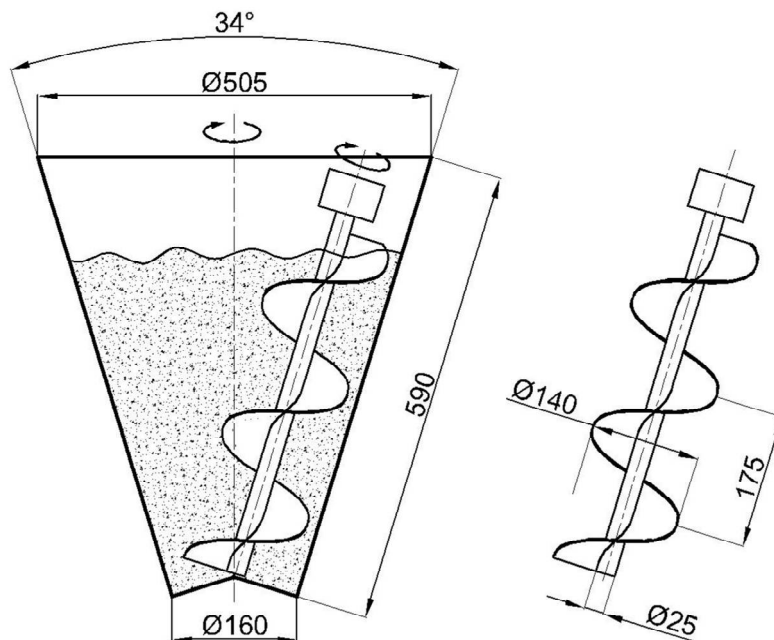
Розміри корпусу і шнека змішувача ПШ-24
